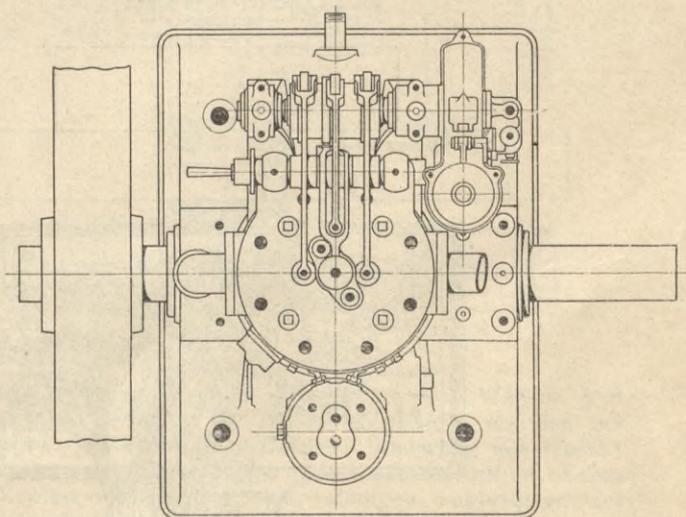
die Brennstoffpumpe einer dreizylindrigen Maschine; sie besitzt selbst drei kleine Pumpzylinder, einen für jeden Kraftzylinder. Der Regulator steht in Verbindung mit drei Rücklaufventilen, welche er während des Druckhubes mehr oder weniger lange offenhält; erst wenn diese Ventile jeweils geschlossen sind, tritt der Brennstoff durch die eigentlichen Druckventile in die Düse über. Die Pumpe wird ebenfalls von der im Gestellkasten befindlichen wagerechten Steuerwelle angetrieben.
